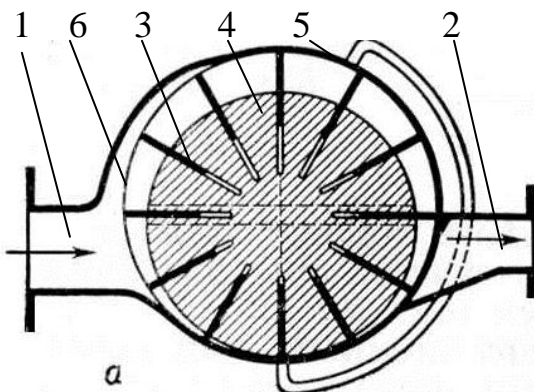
Многопластинчатый роторный насос. 1 - входной, 2 - выходной патрубки, 3 - пластины, 4 - ротор, 5 - корпус, 6 - беговые кольца.
